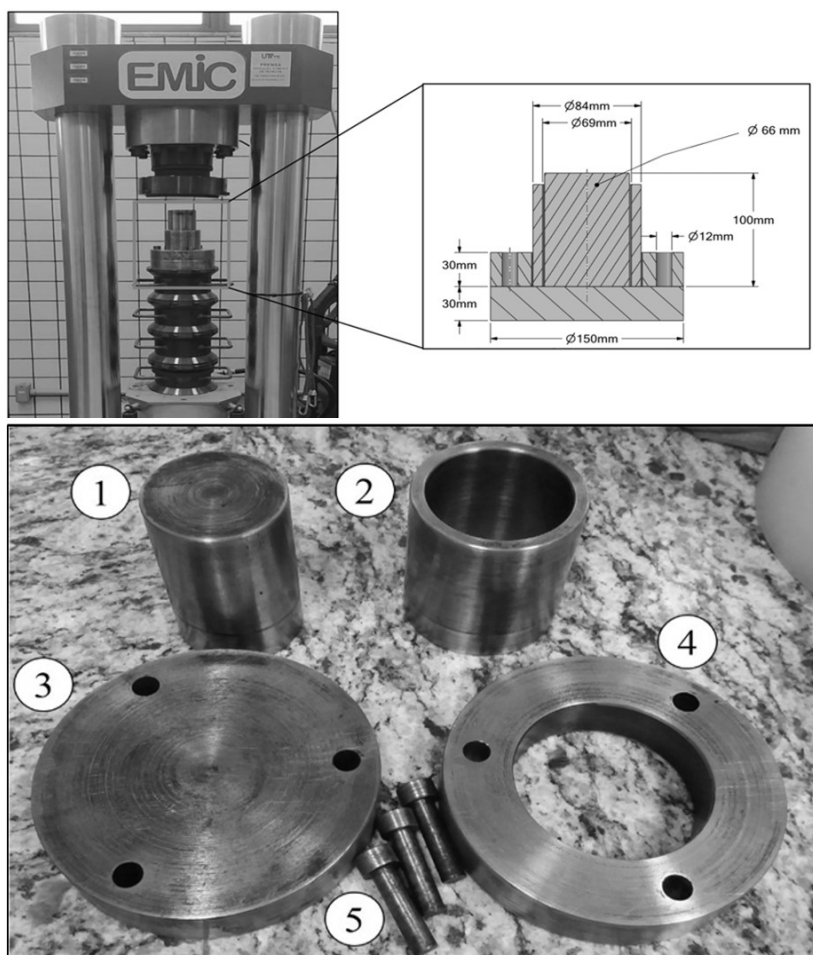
Conjunto do cilindro e a prensa e, detalhes dos componentes do equipamento. 1 – Cilindro maciço de aplicação de carga; 2- Cilindro porta-amostra; 3- Base circular; 4- Anel de fixação; 5- Pinos de fixação.
